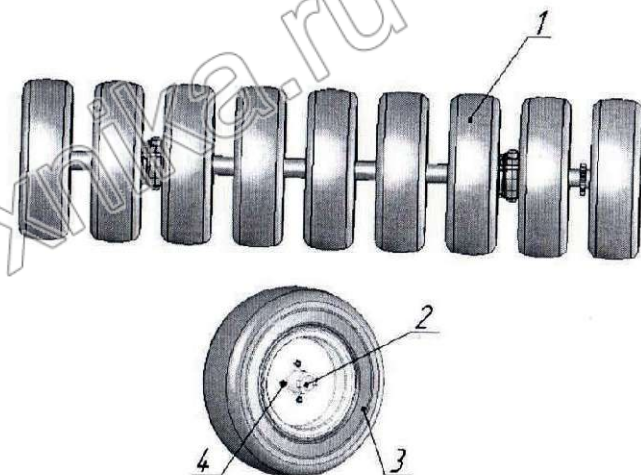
Батарея катков с пневмокатками СКП 01.23.000В
